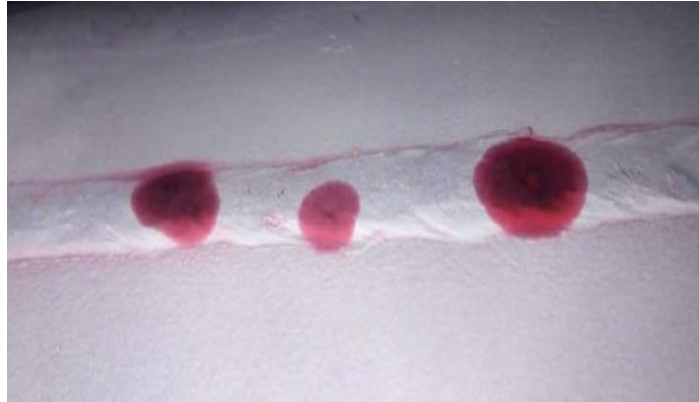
Indicaciones en una grieta de soldadura, fuente propia
